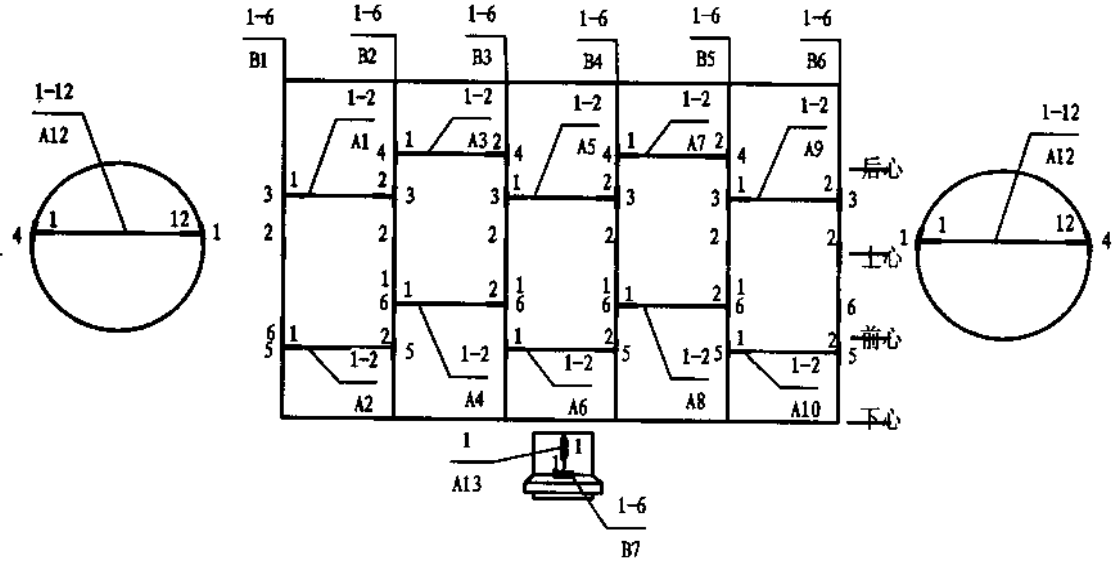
焊缝局部检测部位图 (展开图)
